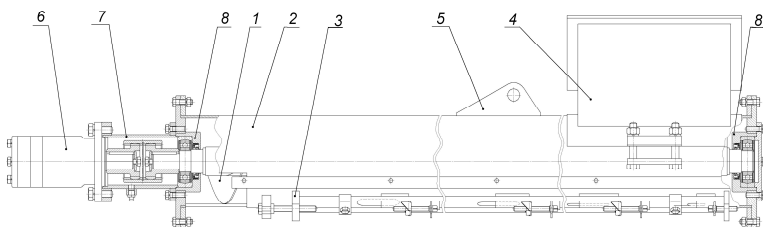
Штанга: 1 – шпек; 2 – кожух; 3 – регулировочное устройство; 4 – загрузочная горловина; 5 – зацеп; 6 – гидромотор; 7 – муфта; 8 – подшипниковый узел
